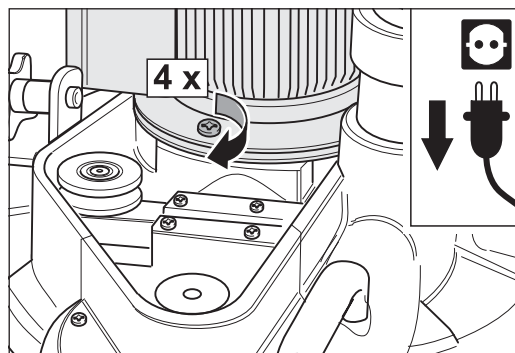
Den Motor mit den vier Schrauben am Maschinengehäuse festschrauben.
